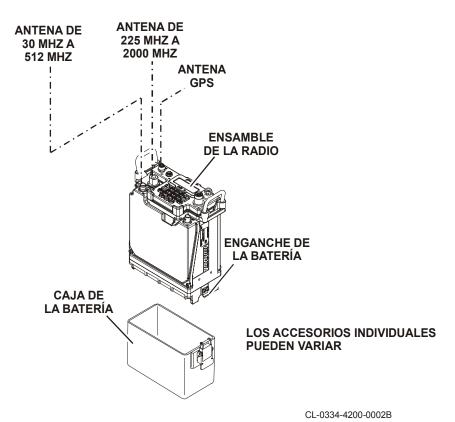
Montaje y Desmontaje del Equipo (Desmontaje/Configuración de Mochila)
